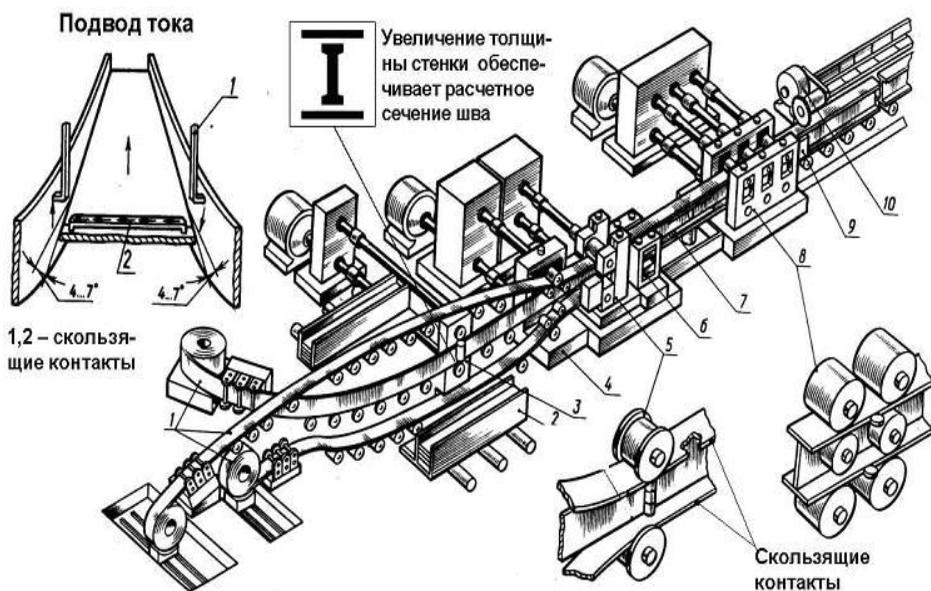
Агрегат для изготовления двутавровых профилей сваркой ТВЧ:
